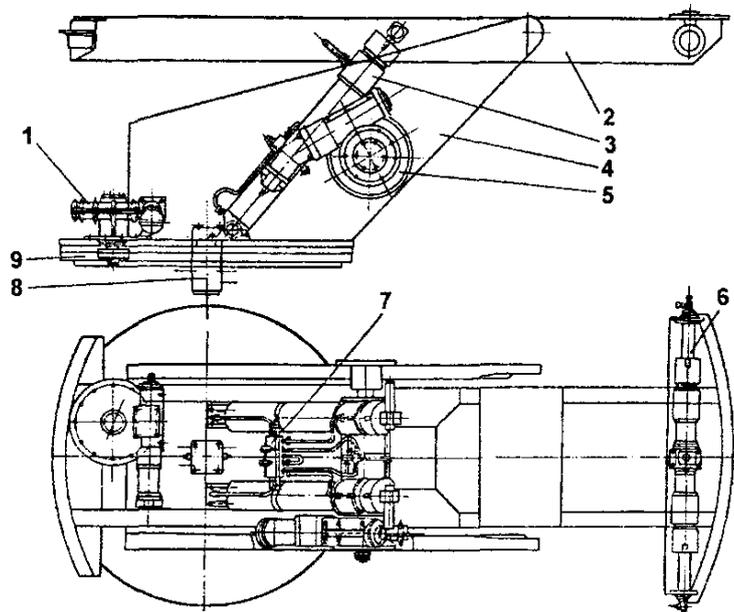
Подъемно-поворотное устройство: 1 - привод поворота; 2 - подъемная рама; 3 - гидроцилиндр подъема; 4 - поворотная рама; 5 - привод выдвигания; 6 - гидроцилиндр бокового выравнивания; 7 - гидрозамок гидроцилиндров подъема; 8 - осевой коллектор; 9 - поворотная опора
